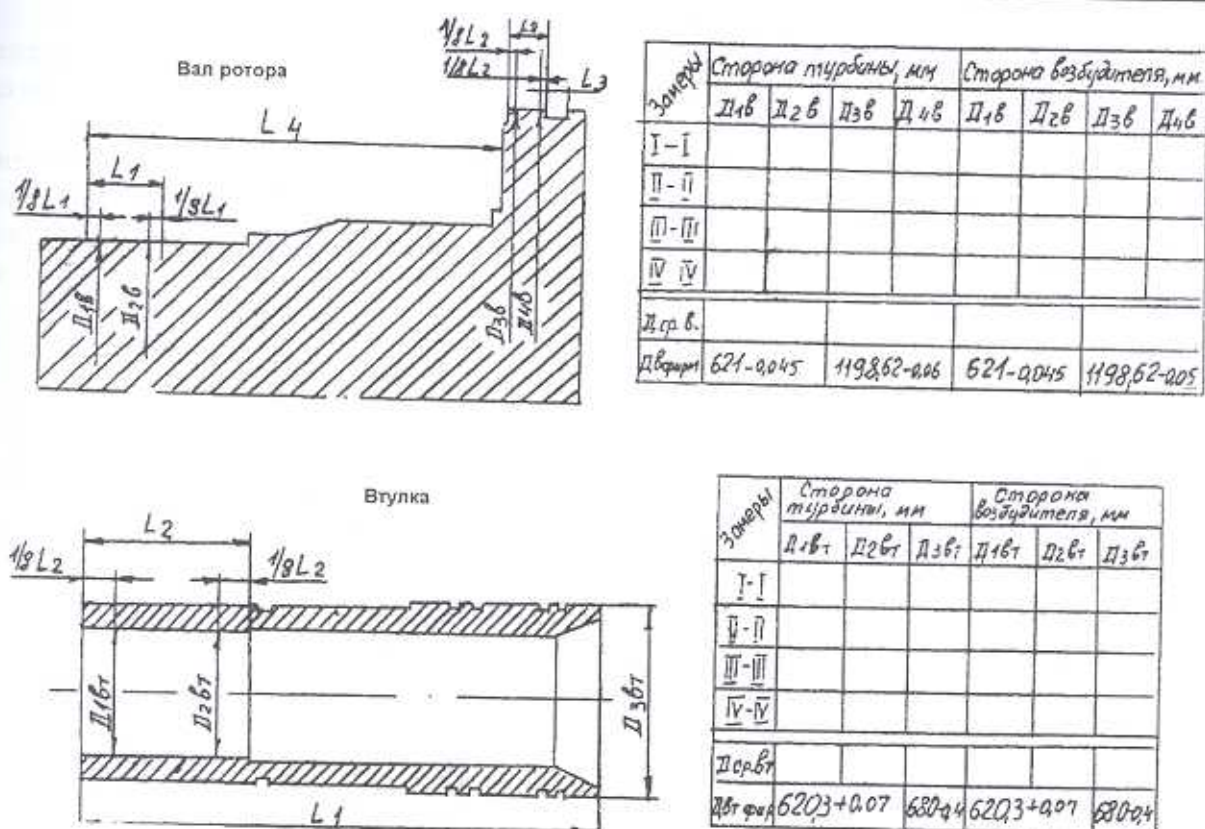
Схема измерений размеров втулки и вала ротора, формуляры
